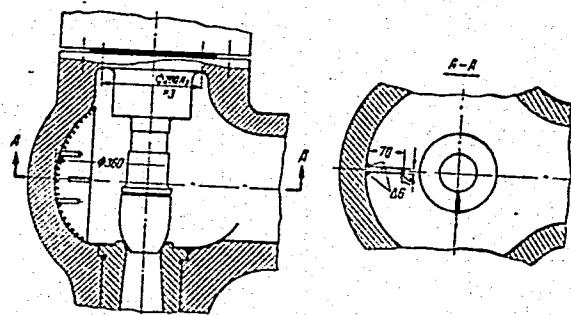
Установка парирного разделителя в паровой коробке клапана.
